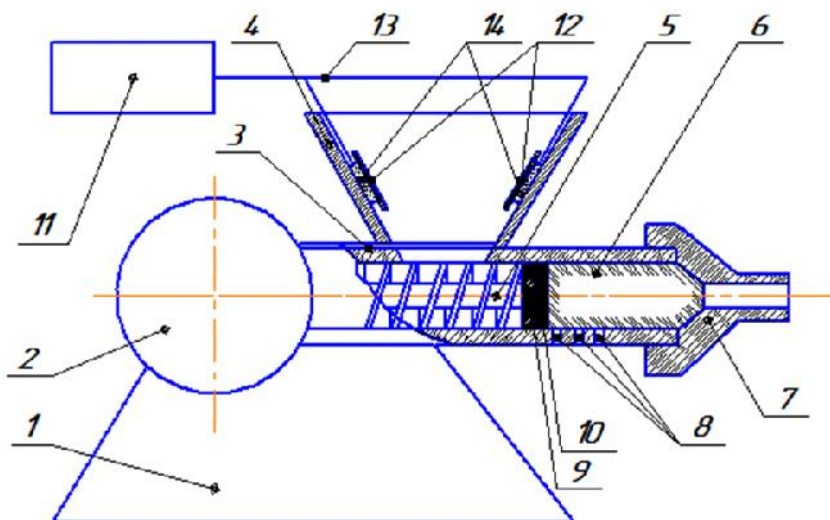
Пресс для изготовления брикетов из подстильного навоза
